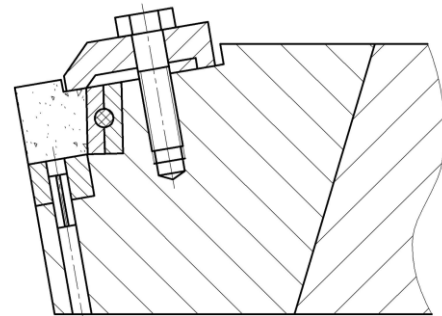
Эскиз блочно-модульного токарного резца с двумя ЭК
